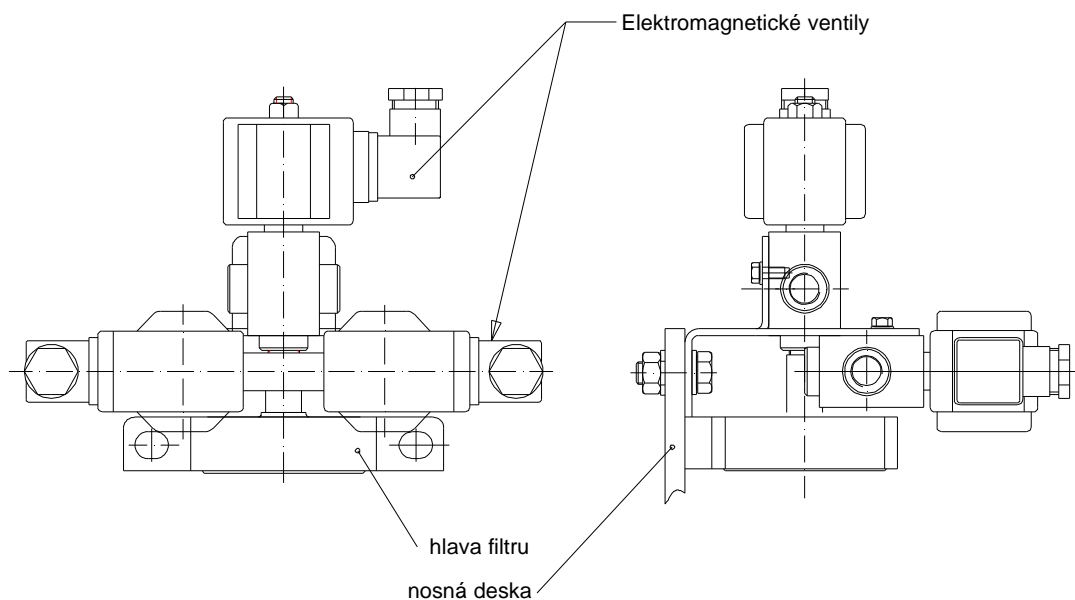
Zapojení předfiltru a pomocného čerpadla
